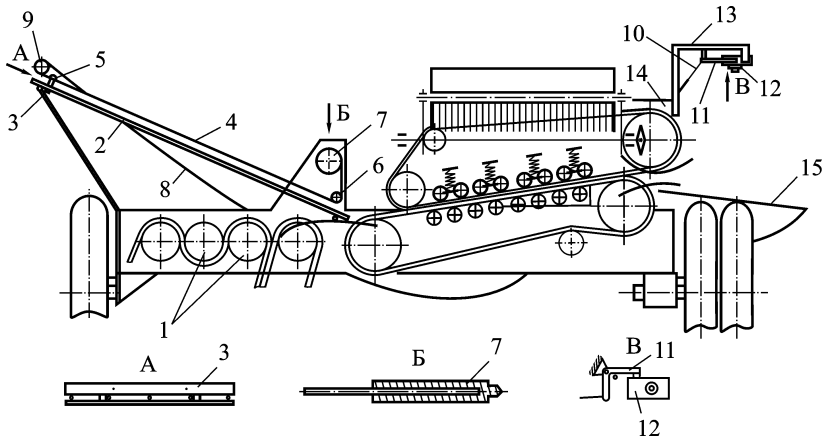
Схема переобладнання льонокомбайна для проведення лабораторних дослідів: 1–бральний апарат; 2–подавальний стіл; 3–поперечна планка; 4–брезентова стрічка; 5–гачки; 6–напрямний ролик; 7–приводний барабан; 8–шпагат; 9–ролик; 10–запобіжна нитка; 11–коромисло; 12–фотоапарат; 13–опора; 14–роздавальний редуктор комбайна; 15–розстилальний пристрій
